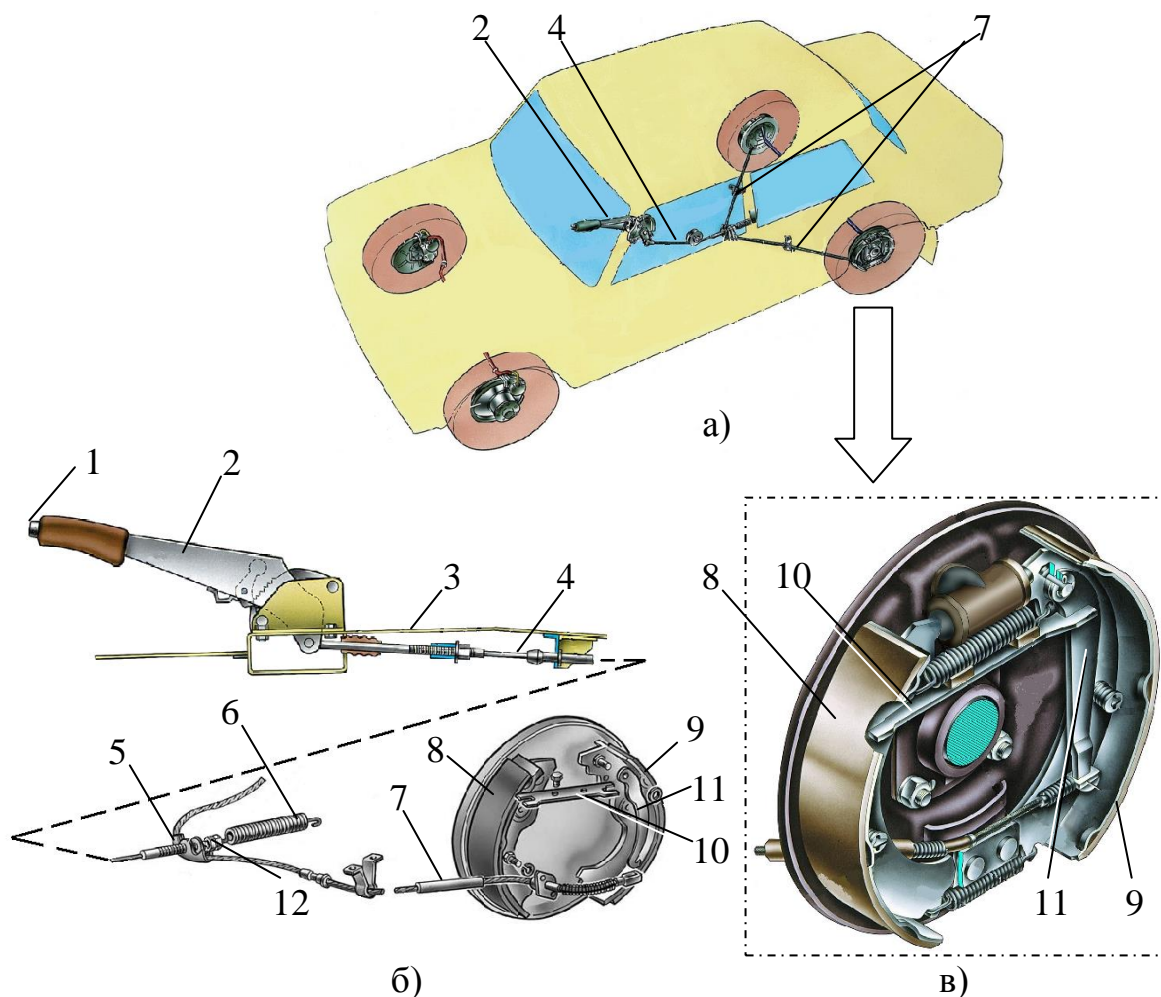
Стояночная тормозная система легкового автомобиля: а – компоновка, б – конструкция, в – привод барабанного тормозного механизма; 1 – кнопка фиксатора; 2 – рычаг; 3 – пол салона; 4 – передний трос; 5 – направляющая заднего троса; 6 – оттяжная пружина; 7 – задний трос; 8 – передняя тормозная колодка; 9 – задняя тормозная колодка; 10 – распорная планка; 11 – рычаг привода тормозных колодок для включения стояночного тормоза; 12 – регулировочная гайка
